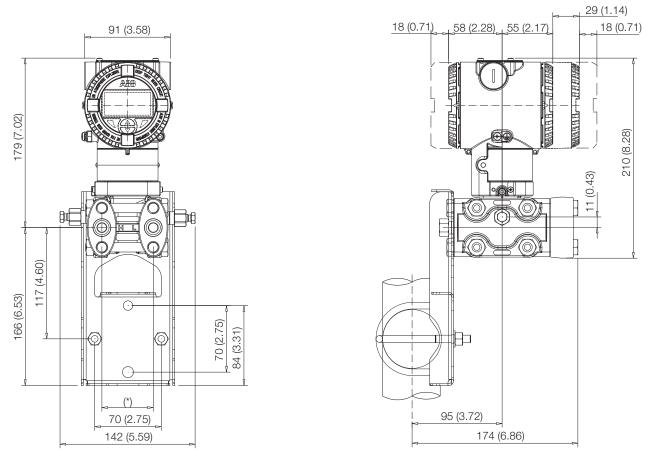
Transmetteur de pression différentielle équipé d'un boîtier de type barillet installé sur un tuyau avec support de montage en inox de type plat (B5) en option
